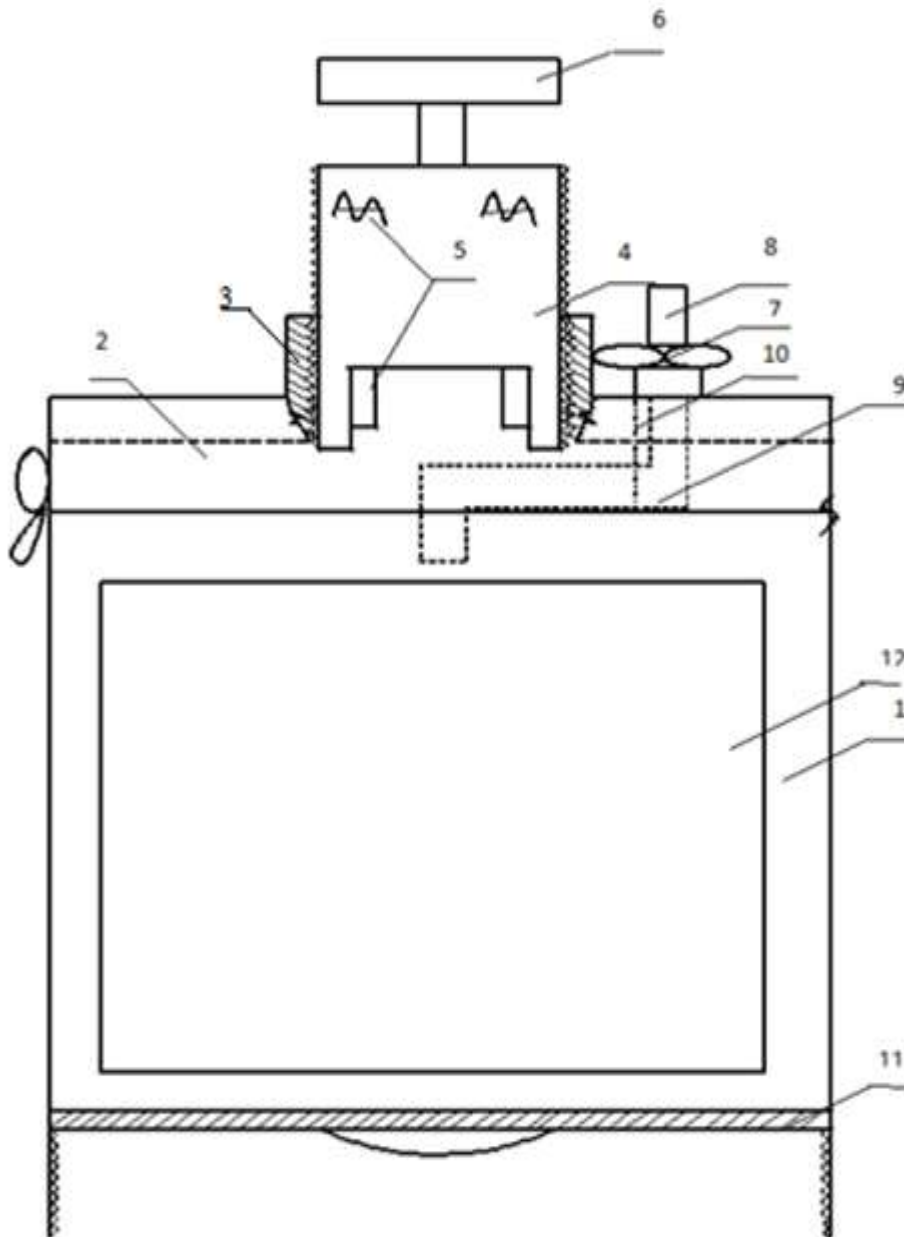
Принципова схема машини для розливу та закупорювання свіжовидоєного молока: 1 – тубус; 2 – кришка; 3 – виступаюча горловина; 4 – циліндр; 5 – гвинтові затискачі; 6 – ручка; 7 – кран для контролю кількості залитої рідини; 8 – труба; 9 – заливна труба; 10 – Г-подібний гак; 11 – днище; 12 – вікно для перевірки кількості налитого молока.
